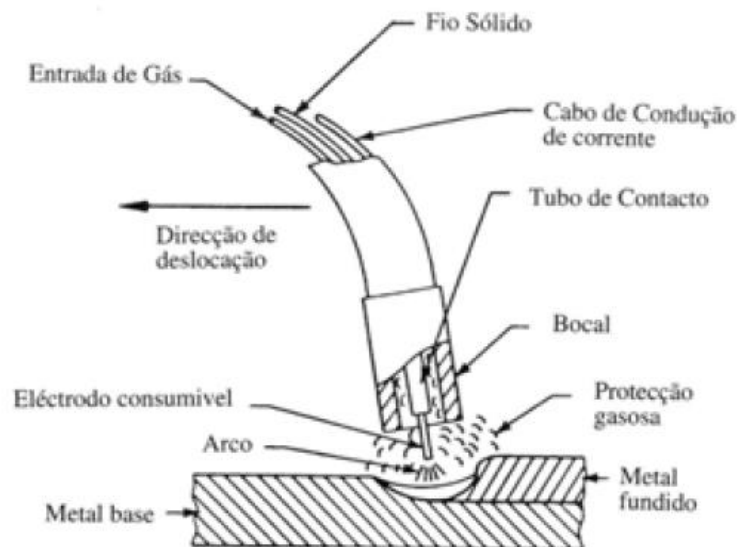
Princípio de funcionamento da soldadura MIG/MAG [42]
